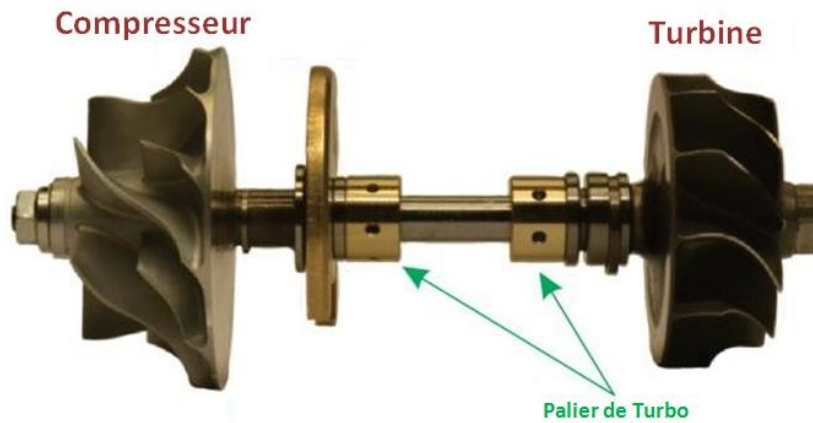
Modèle d'assemblage du palier de Turbocompresseur
